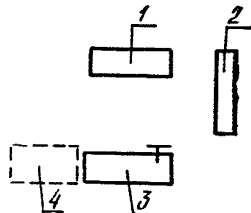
Типовая схема планировки рабочего места разборки и сборки механизма рулевого управления
